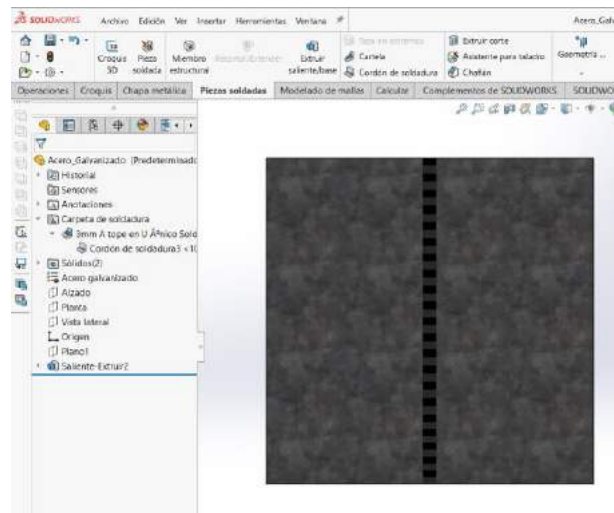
Cordón de soldadura en las placas de acero galvanizado
